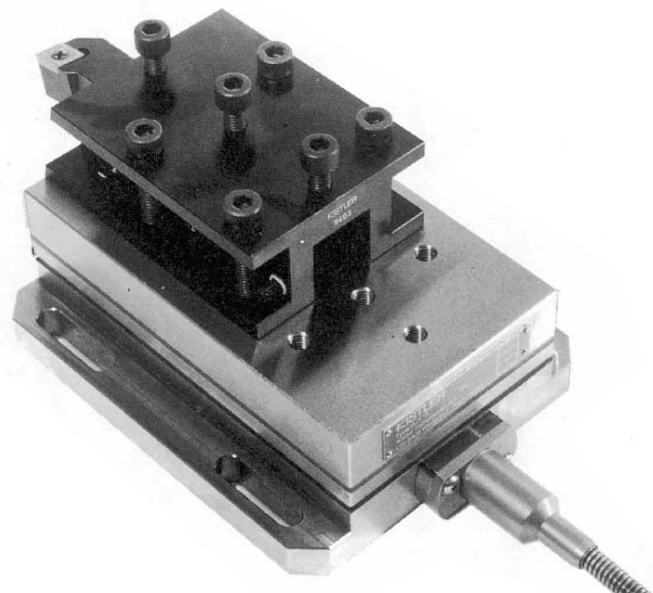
3-Komponenten-Kraftmessplattform mit Werkzeughalter (Quelle: Kistler Instrumente AG)
